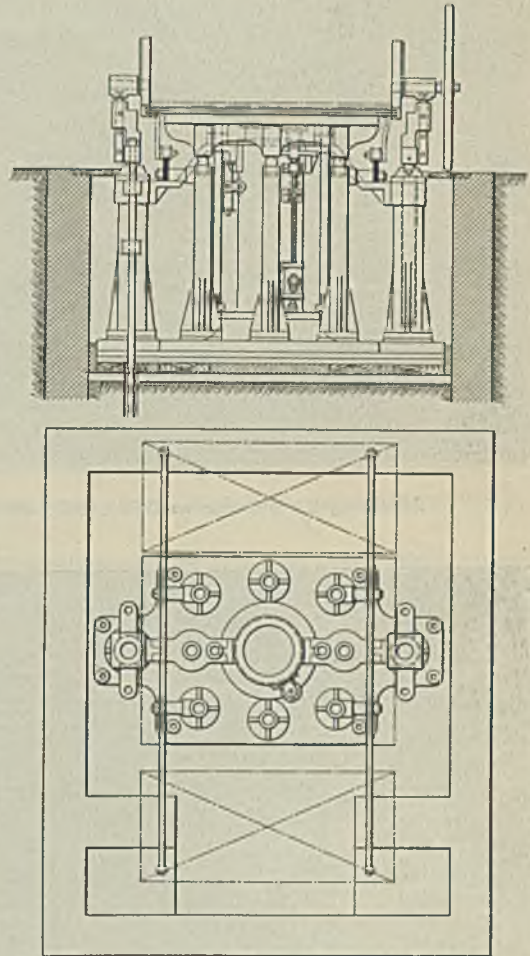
Ansicht und Grundriß einer Maschine für Formkästen von 1300 × 1300 × 600 mm.
